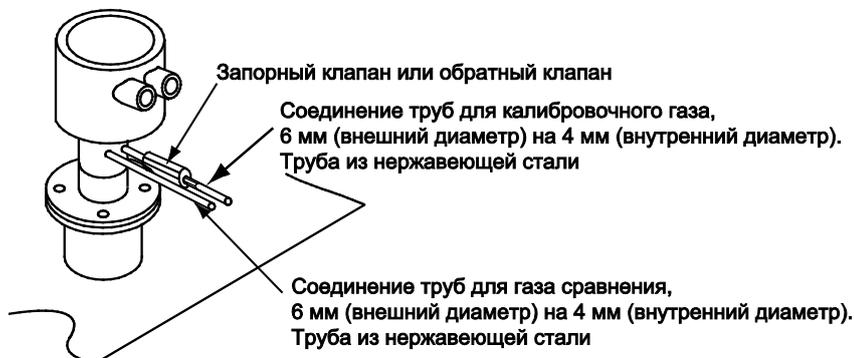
Трубная обвязка для входа калибровочного газа
